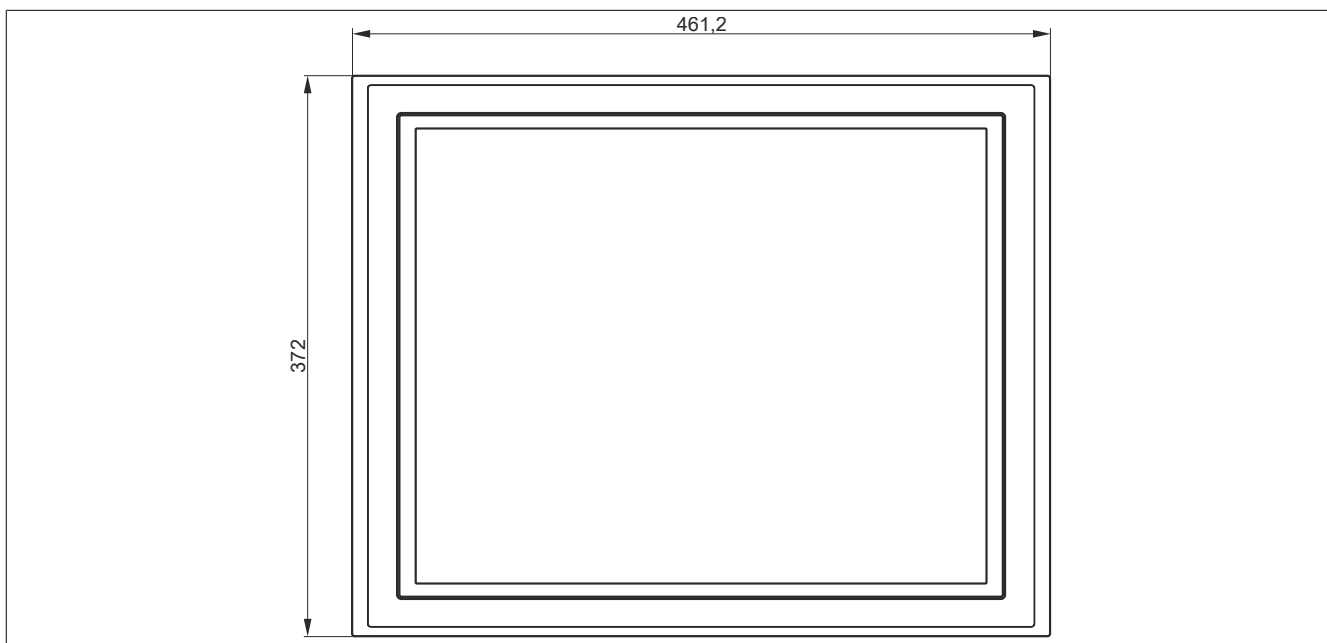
5AP5120.1906-000 - Abmessungen
